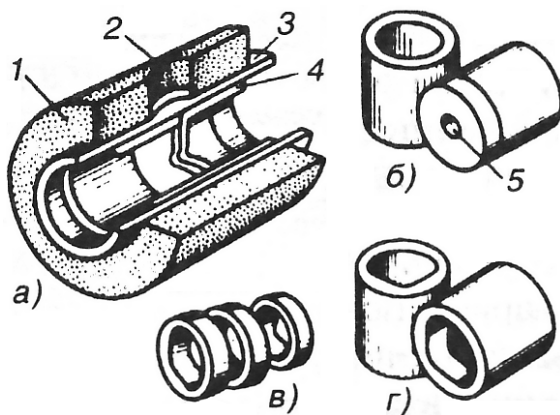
Патрон ПА (а) і деталі до нього для термітного зварювання:
